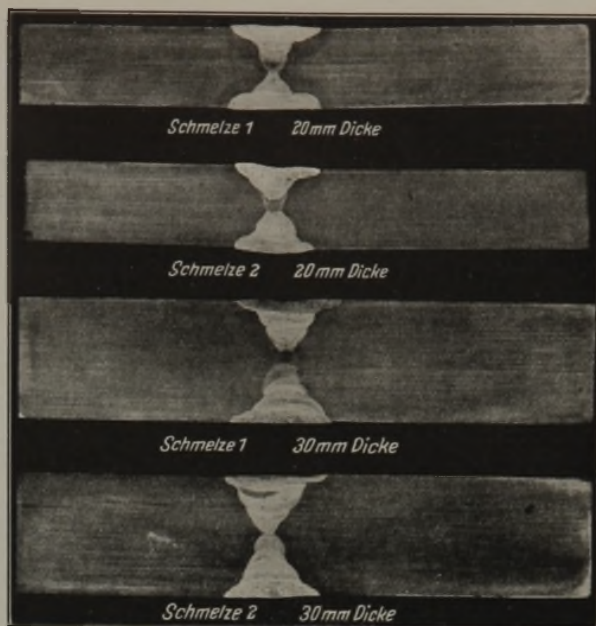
Makrogefüge von X-Naht-Schweißungen an Mangan-Phosphor-Stahl.
